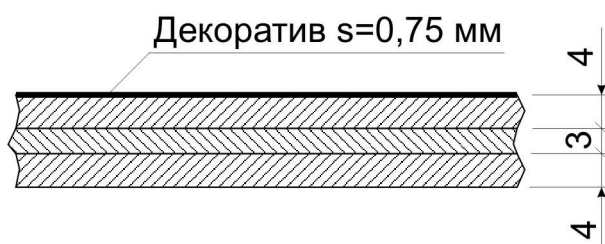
Сечение многослойной обшивки борта судна из композитов
